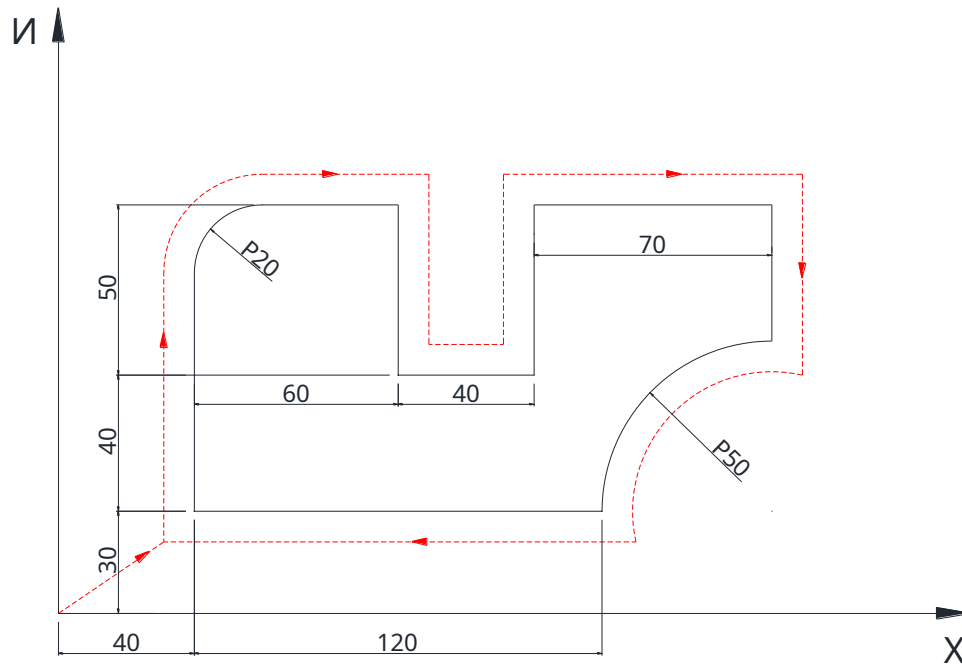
Эскиз 3 процесса обработки заготовки
